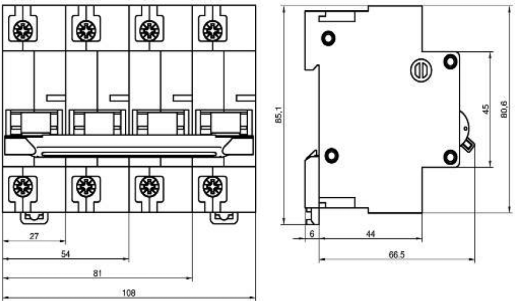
Габаритные, установочные, присоединительные размеры выключателей.
